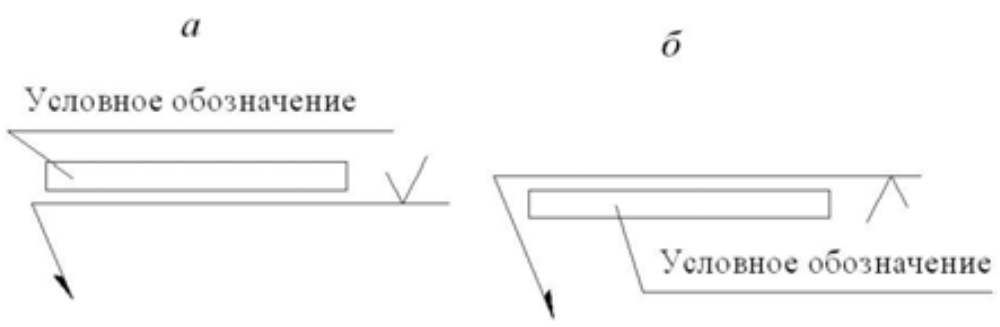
Обозначение шероховатости механически обработанной поверхности шва: а – с лицевой стороны; б – с оборотной стороны
